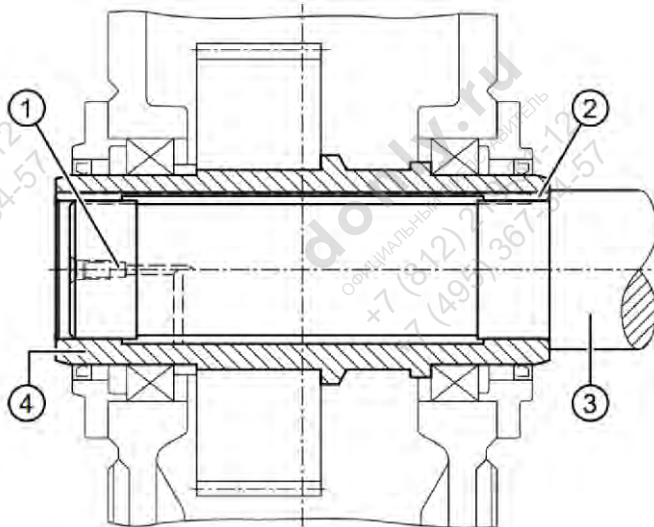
б: Подготовка редукторов с полым валом и шпоночным пазом
